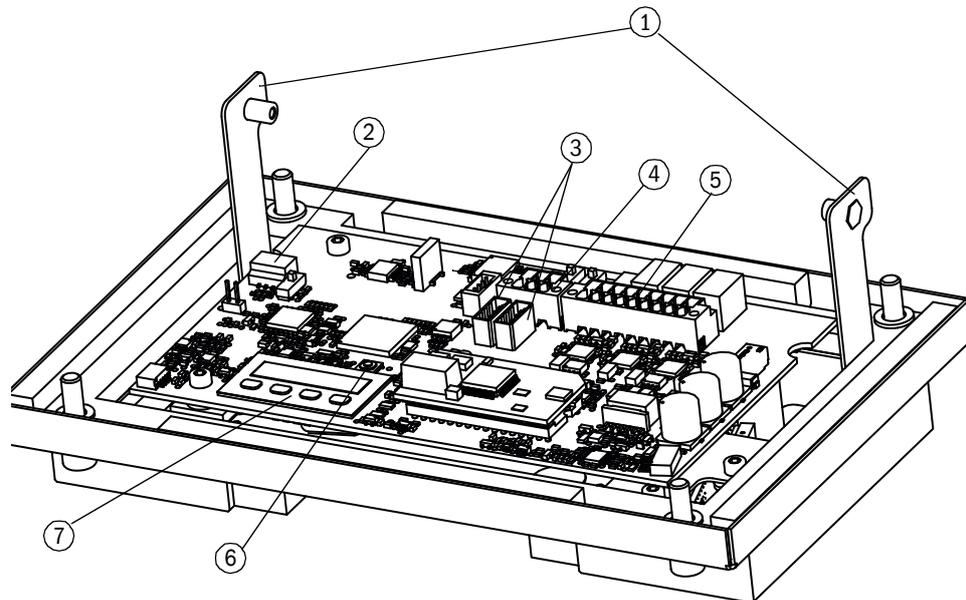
Innenansicht Gehäuseabdeckung ohne Heizung
